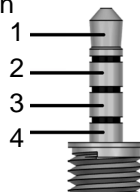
Цоколёвка разъёма Jack F 3.5mm 4pin
